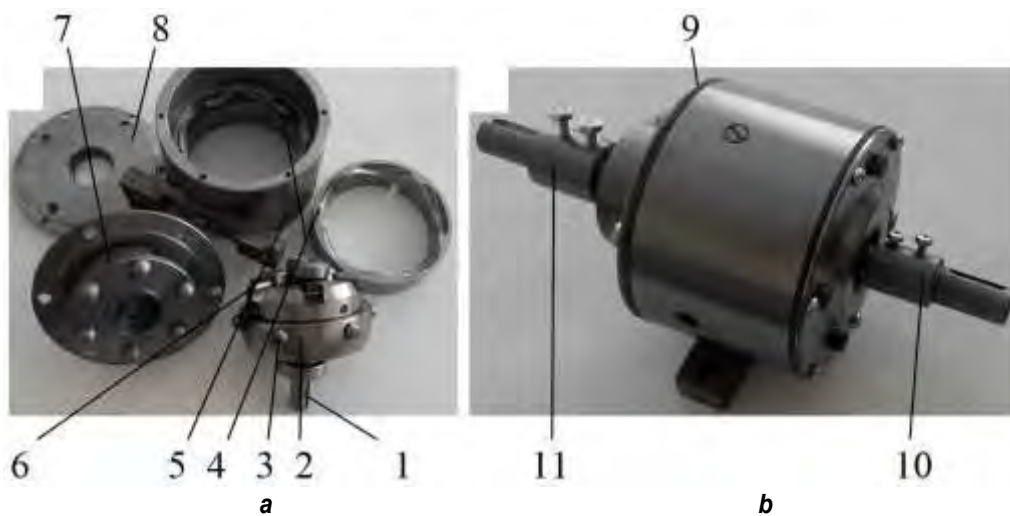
Экспериментальный образец редуктора СРП: основные детали и узлы (а); редуктор в сборе (б): 1 – ведущий вал; 2 – генератор; 3 – тела качения (ролики);
